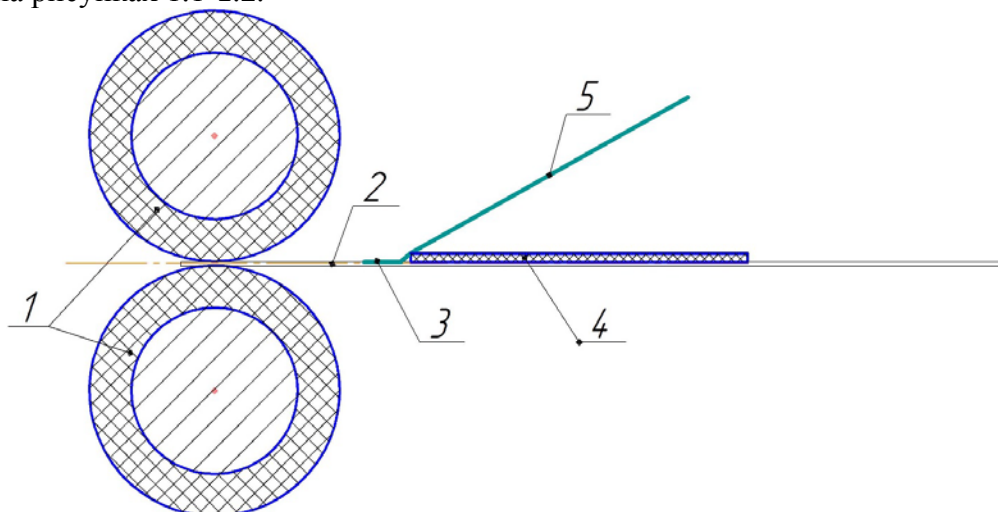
Пакет, заправленный в ламинатор до начала накатки
